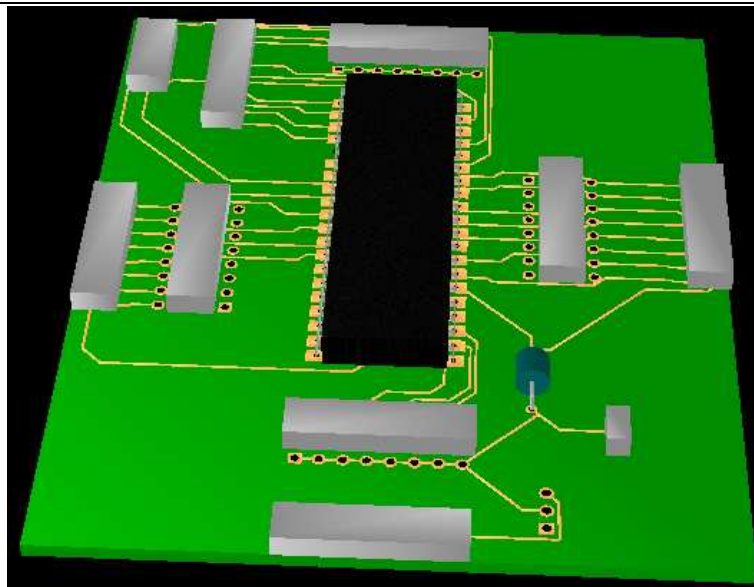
Muestra en tercera dimensión de la tarjeta de sensado
